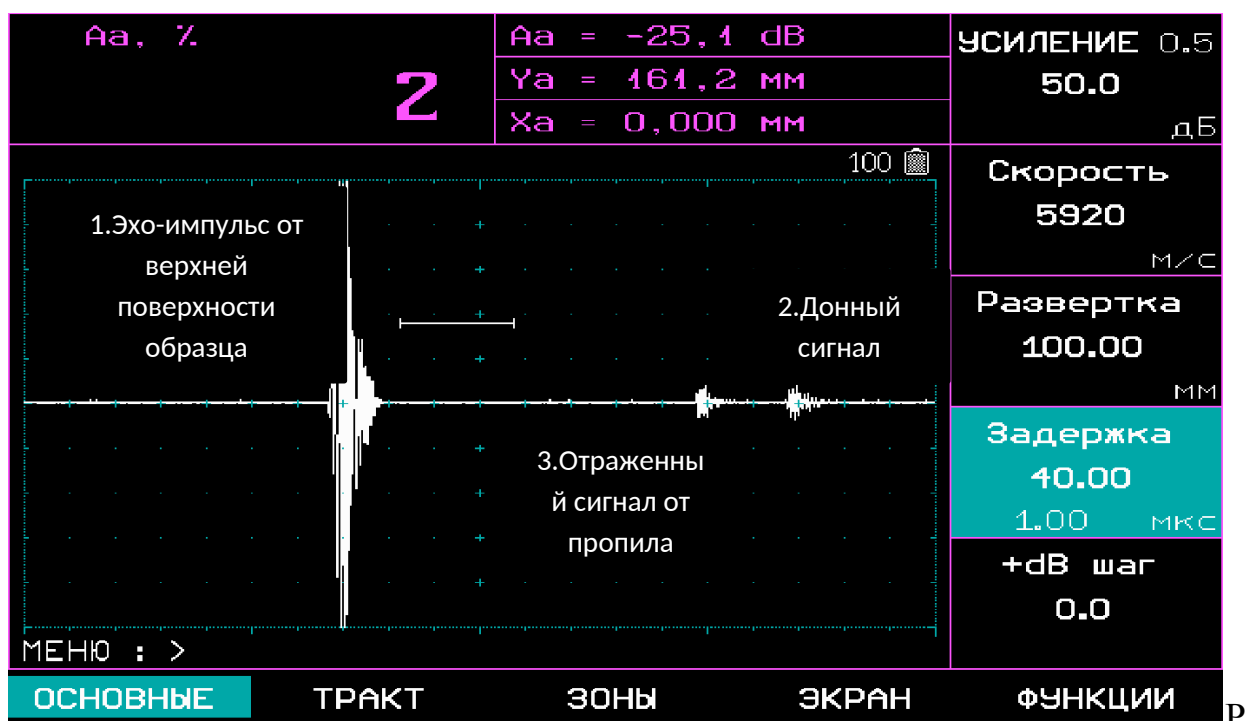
изображение А-развертки калибровочного образца в области близко расположенных пропилов.
